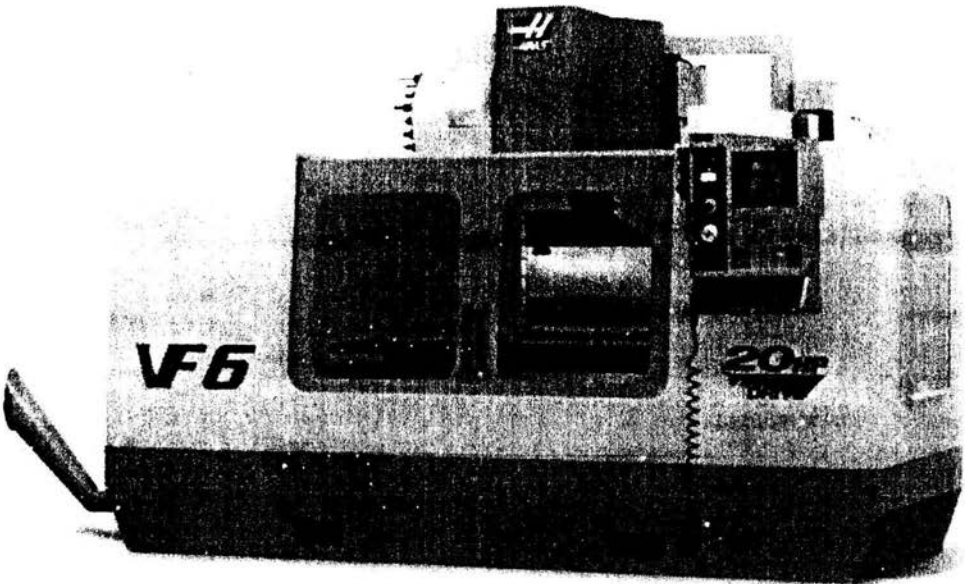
Maquina CNC (Centro de maquinado)
